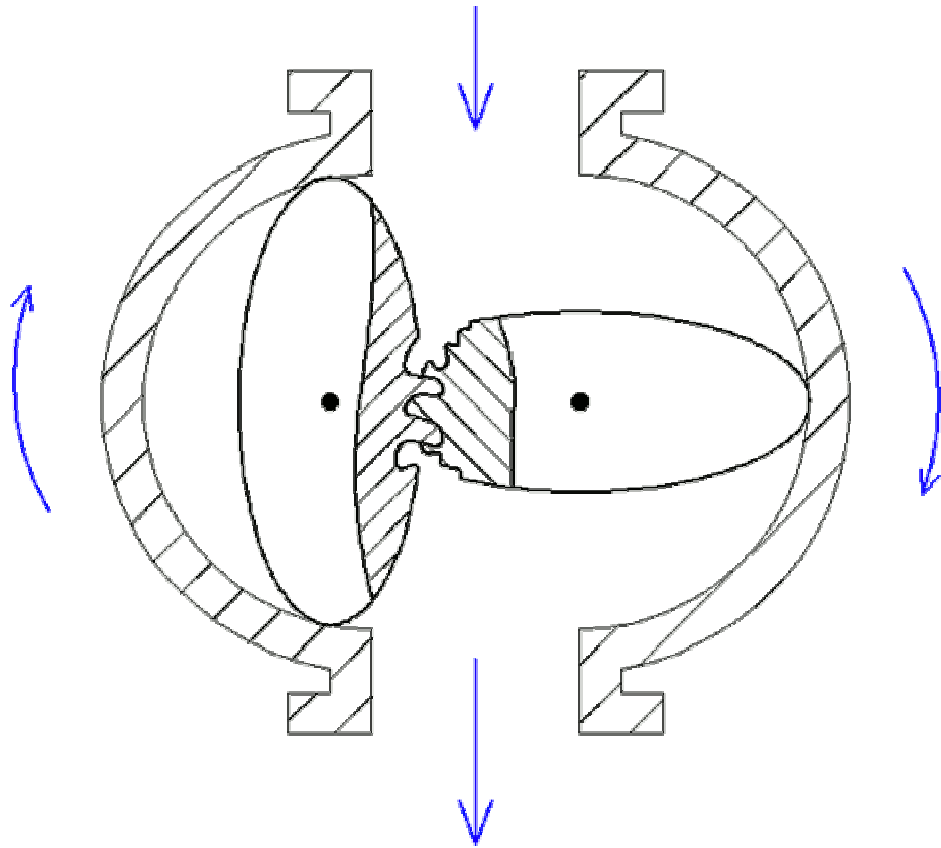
Схема зубчастого лічильника із овальними шестернями.
